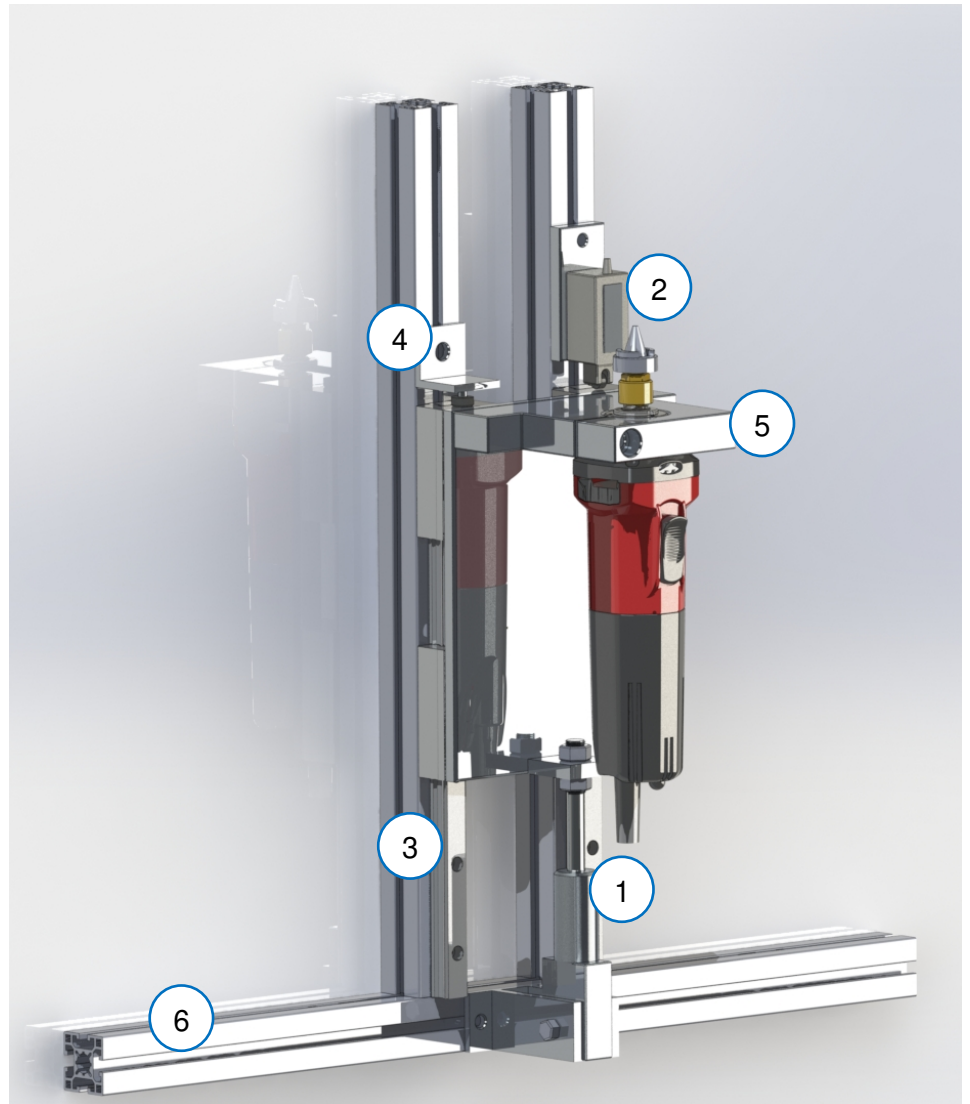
Baugruppe Antriebsmechanik Kernkomponenten
